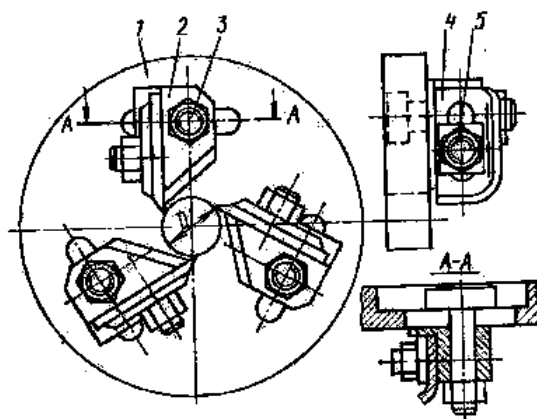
Ножевая головка круглопалочного станка: *1* — корпус, *2* — резцедержатель, *3*, *5* — болты,
